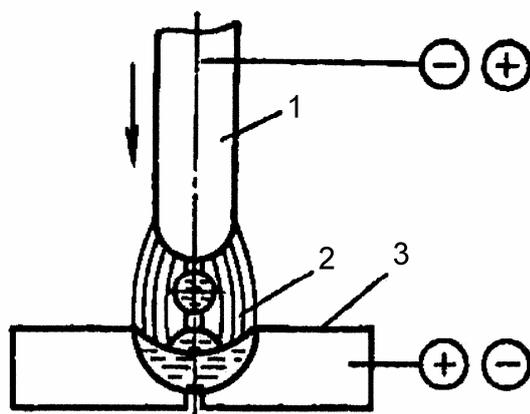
Электродуговая сварка по методу Славянова:
